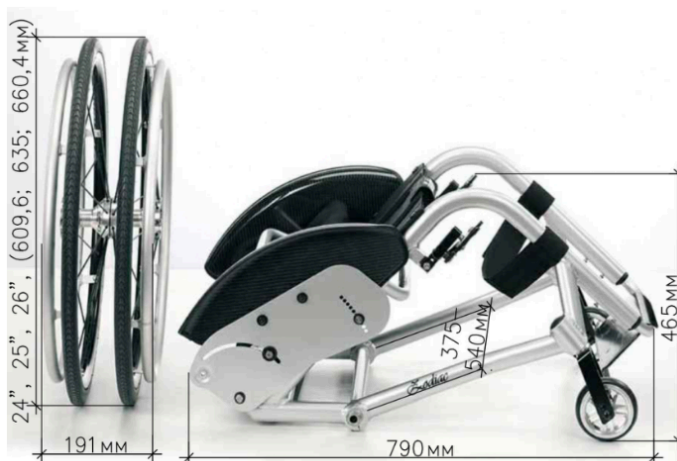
Спортивная коляска для фехтования в транспортировочном виде. Размеры при транспортировке
